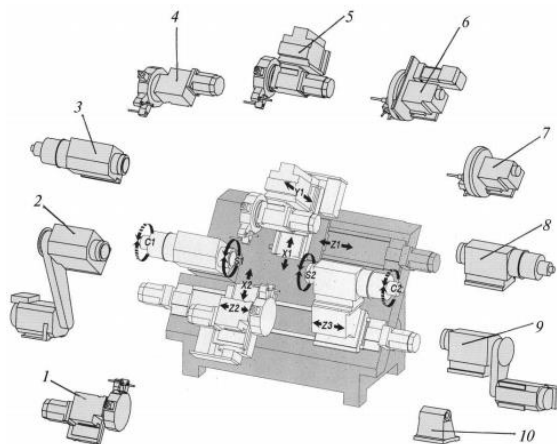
Базова компоновка і набір можливих модулів для токарного багатоцільового верстата з ЧПК фірми Schaublin (Швейцарія)
